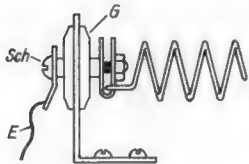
Befestigung der Feder am Haltewinkel. Sch = Maschinenschraube, E = Erdleitung, G = Gummipuffer
